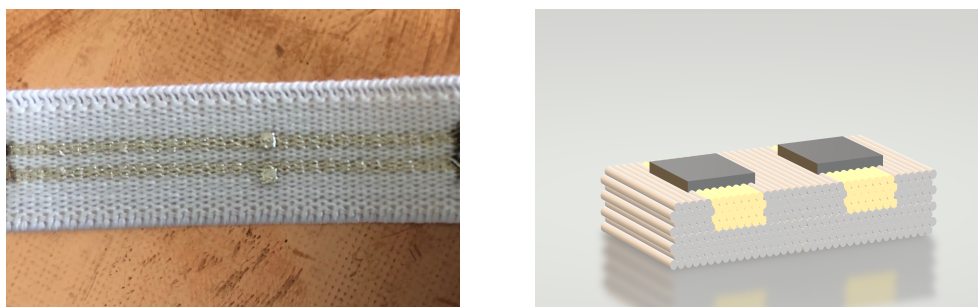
Kontaktování pájením - Zapouzdření nevodivým lepidlem
